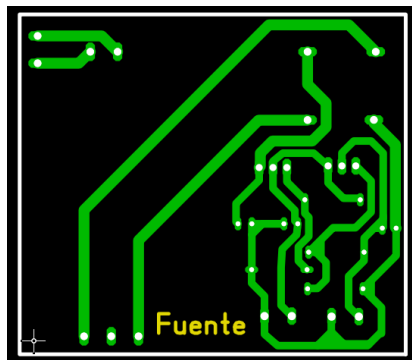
, Diseño PCB Fuente en Sprint Layout. Fuente: elaboración propia de los autores
